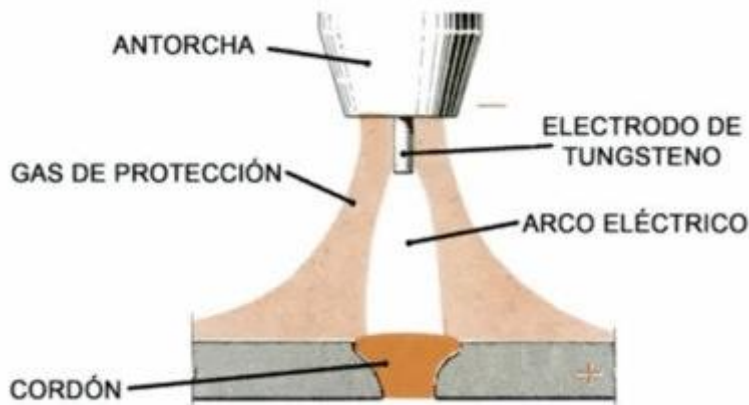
Elementos de la soldadura TIG (SOLDADURA.TOP, 2021)
